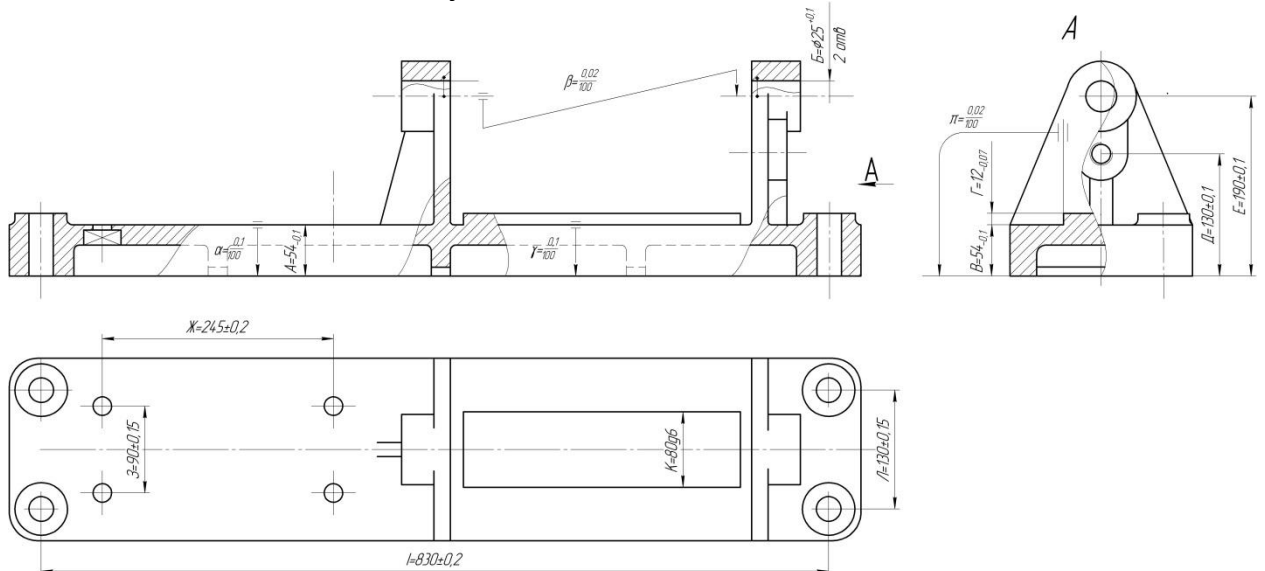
Розмірні зв'язки корпусу, які необхідно вирішити під час механічної обробки станини
